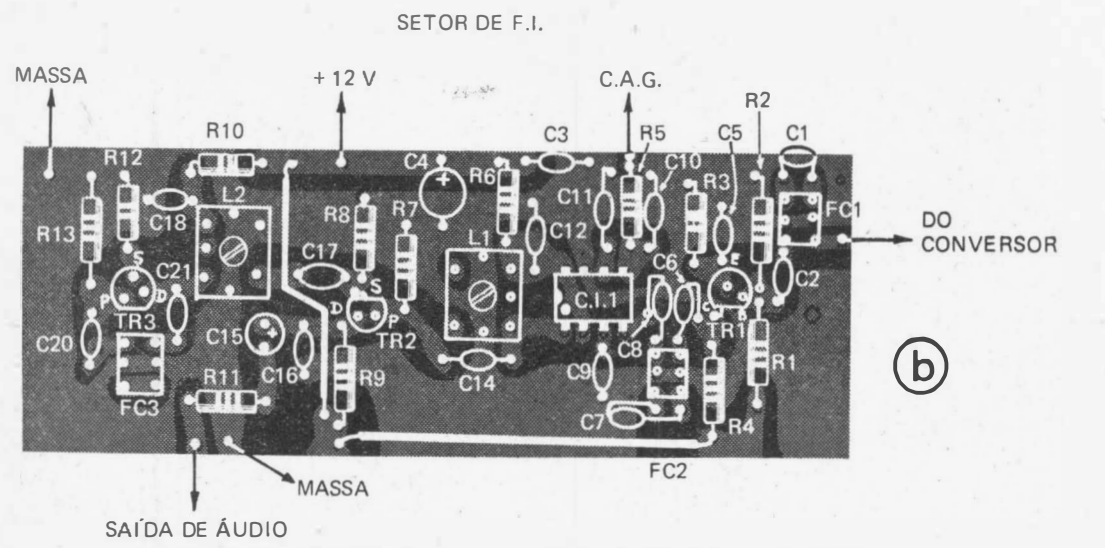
Disposição dos componentes sobre a plaqueta do canal de F.I.
